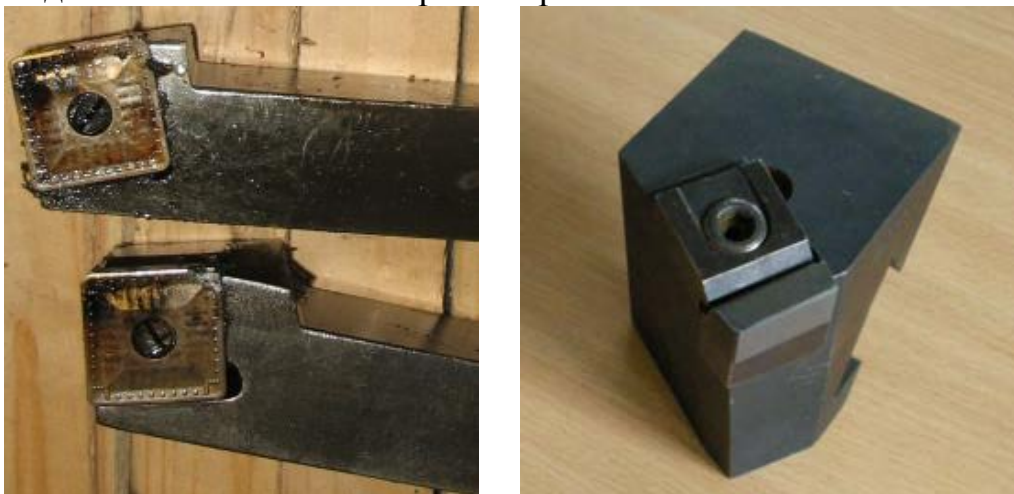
Конструкції токарних різців для обточування деталей на важких верстатах
